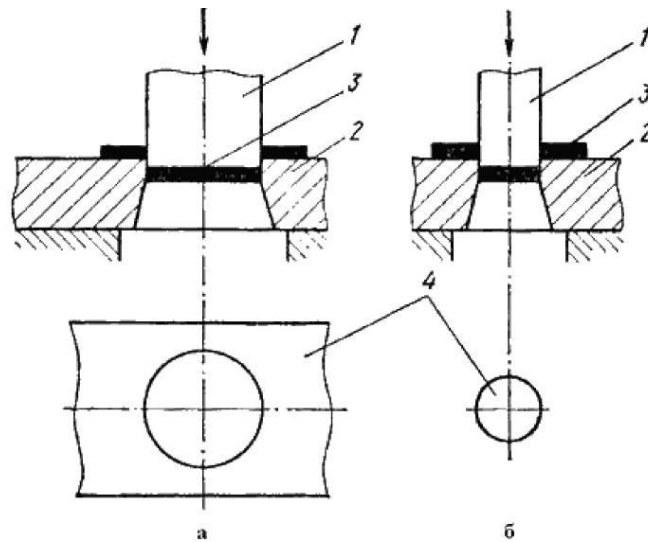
Схема процессов вырубki (а) и пробивки (б)
